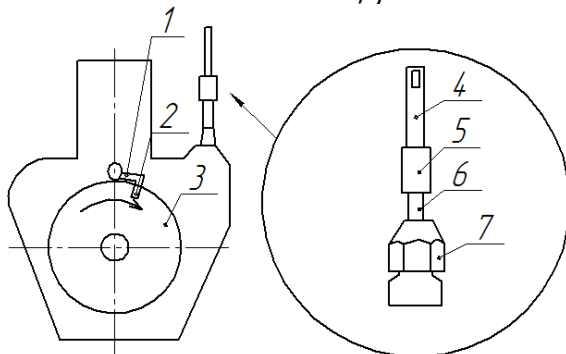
Схема к проверке установочного угла опережения впрыска топлива
